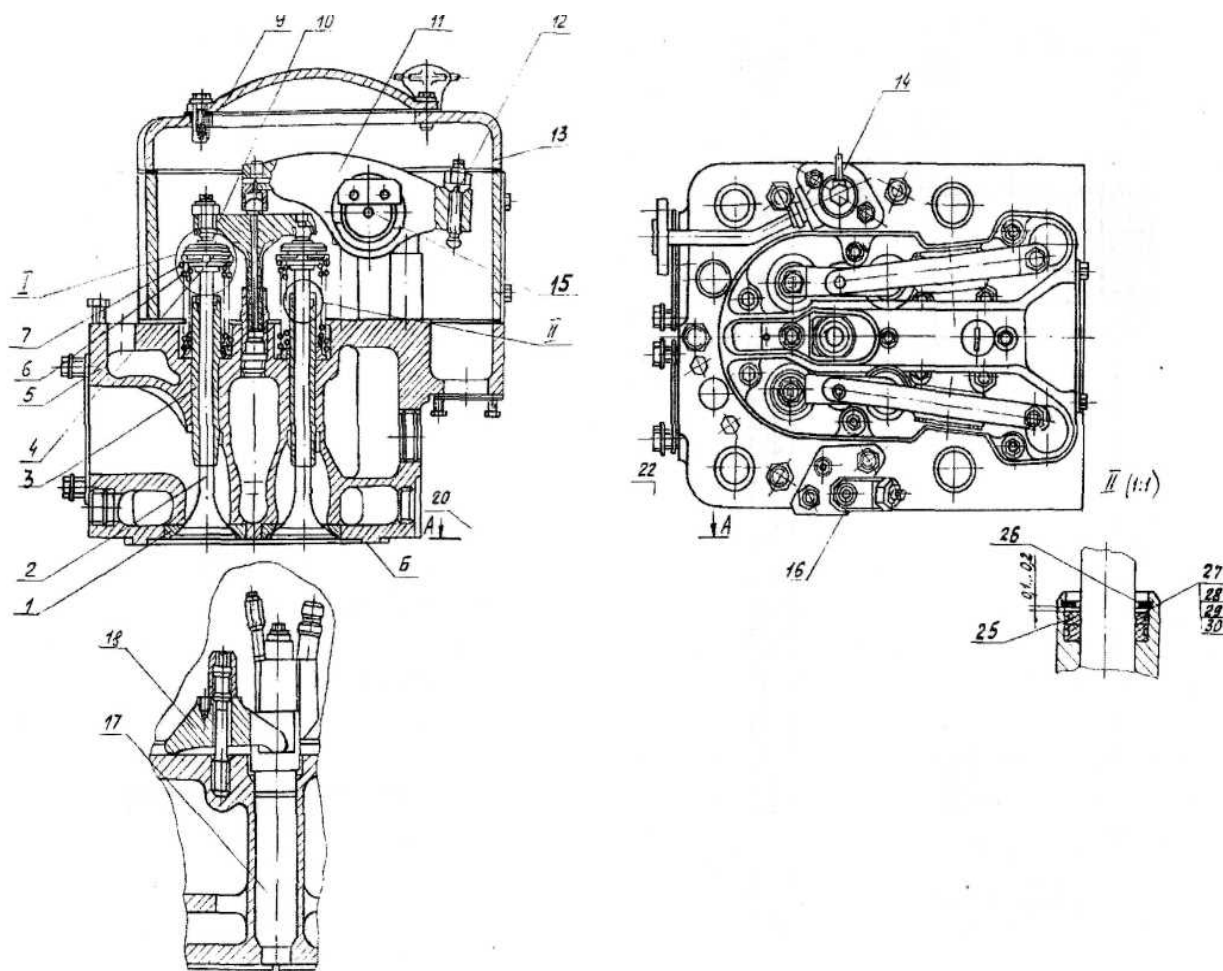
Кришка циліндру двигуна: 1 - сідло клапана; 2 - клапан впускання (випуску); 3 - направляюча клапана; 4 - механізм повороту клапанів; 5 - кришка; 6 - пружина внутрішня; 7 - пружина зовнішня; 9 - кришка; 10 - траверса; 11 - коромисло; 12 - регулювальний гвинт; 13 - закриття; 14 - пусковий клапан; 15 - вісь; 16 - індикаторний кран; 17 - форсунка; 18 - скоба форсунки; 25 - фторопластові кільця; 26 - стопорне кільце; 27, 28, 29, 30 - кільця
